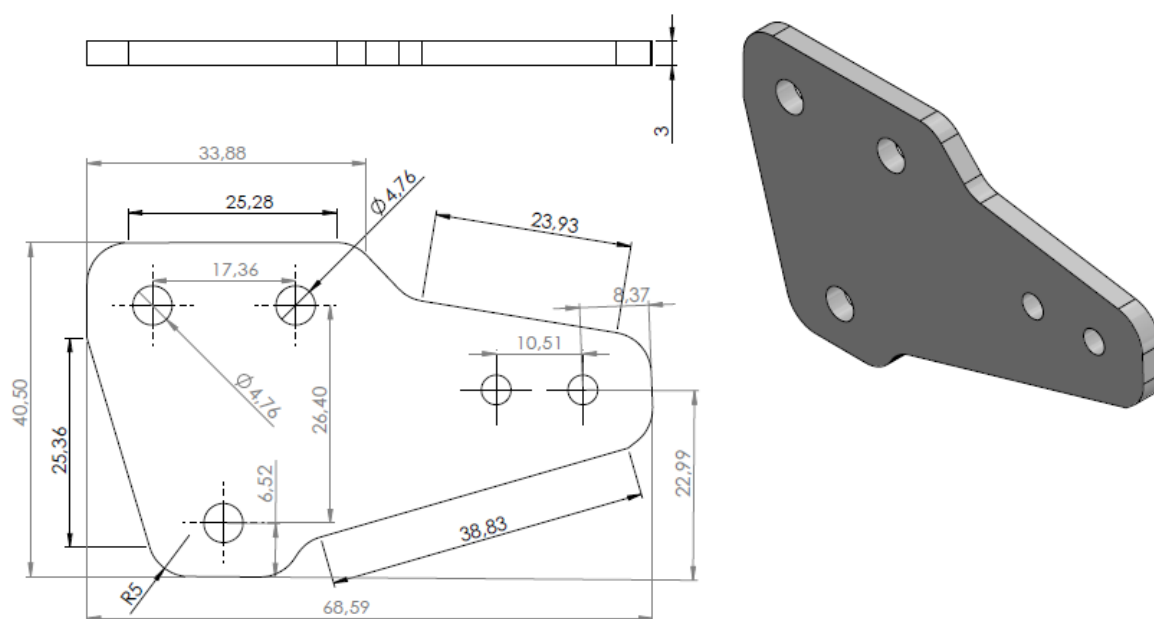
3D модель крепления баз гексакоптера в SolidWorks
